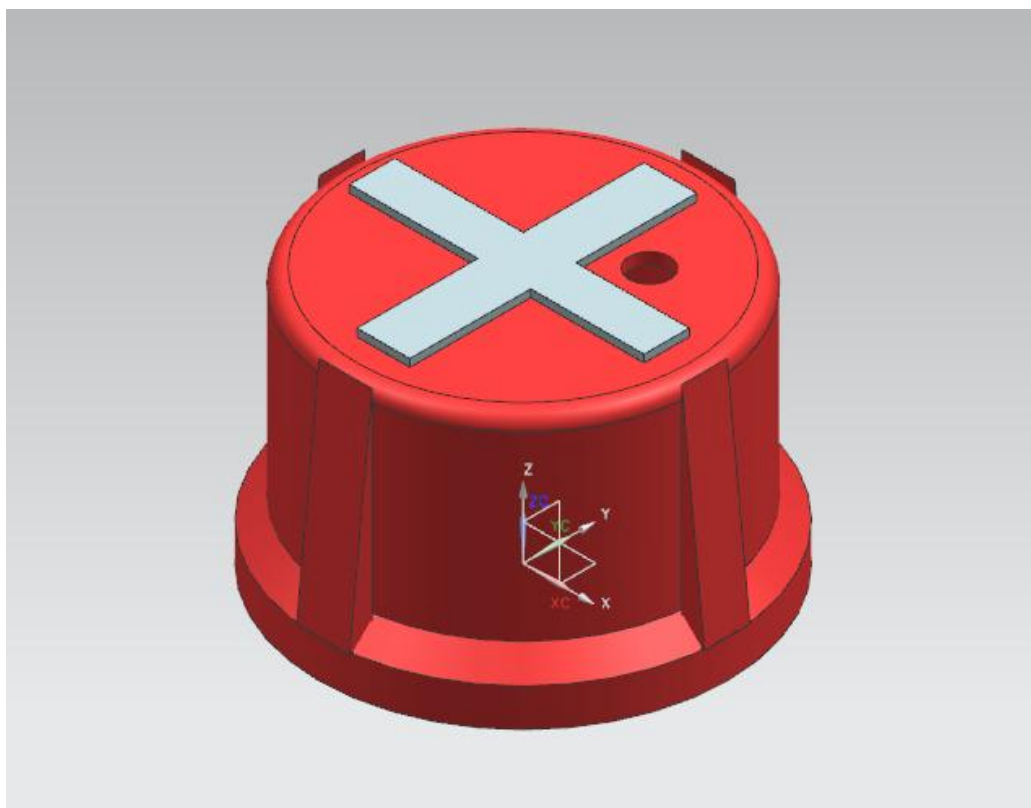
Vista isométrica CAD de la pieza a inyectar
